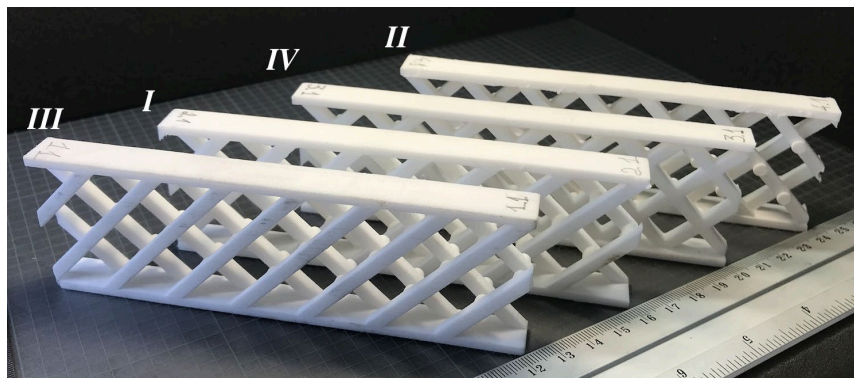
Изготовленные трехслойные образцы с сетчатыми заполнителями различной структуры
